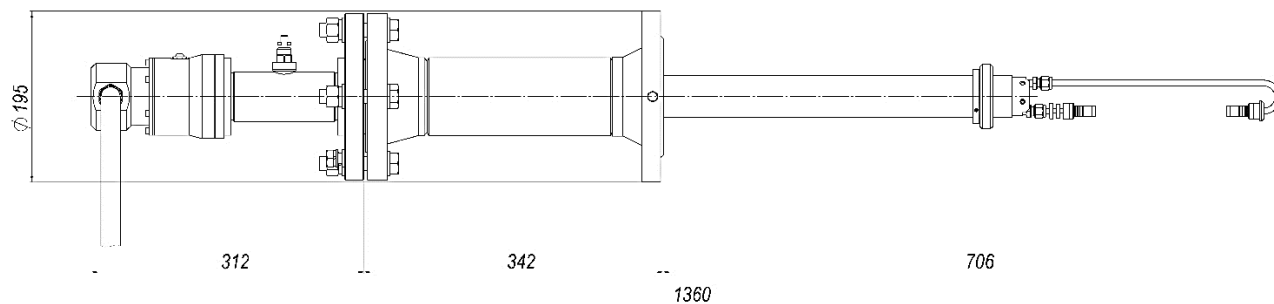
Габаритные размеры приемопередатчика КТМ100 ПР ЛБ
